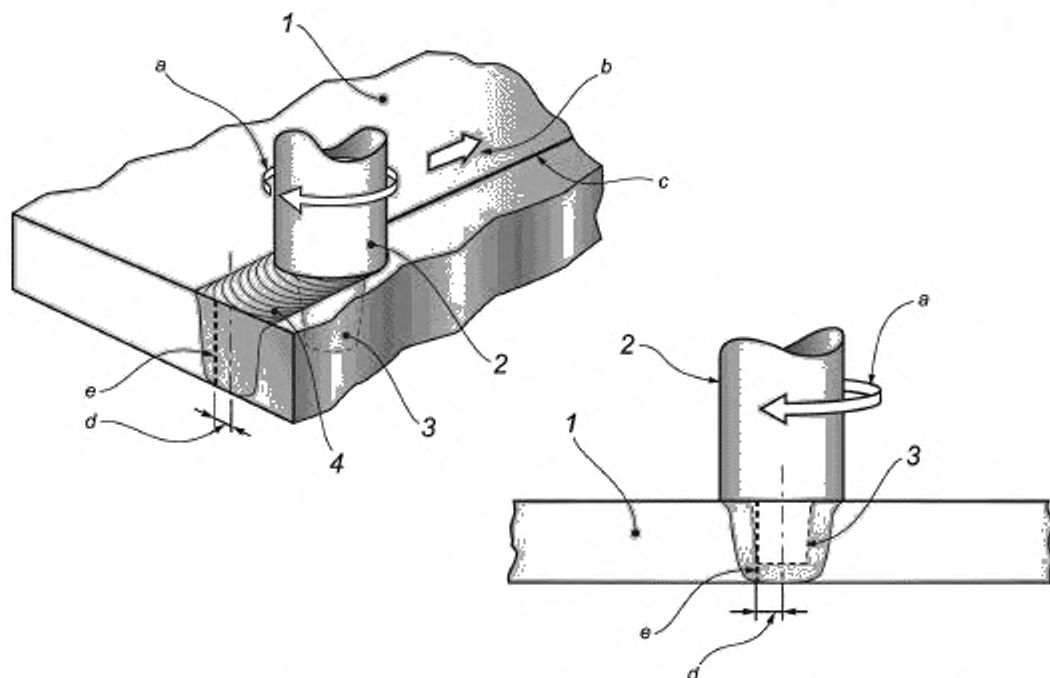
Внешний вид стыкового сварного шва, демонстрирующий непровар
